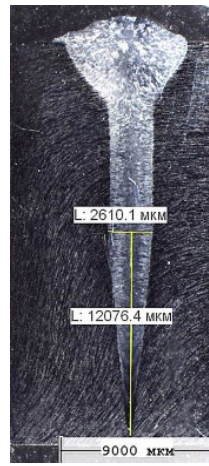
Схема замеров геометрии сварного шва
